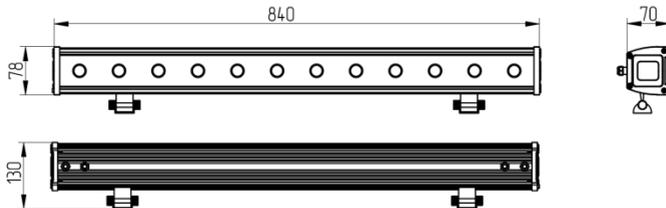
Габаритные размеры линейного прожектора RGBW 48W.
